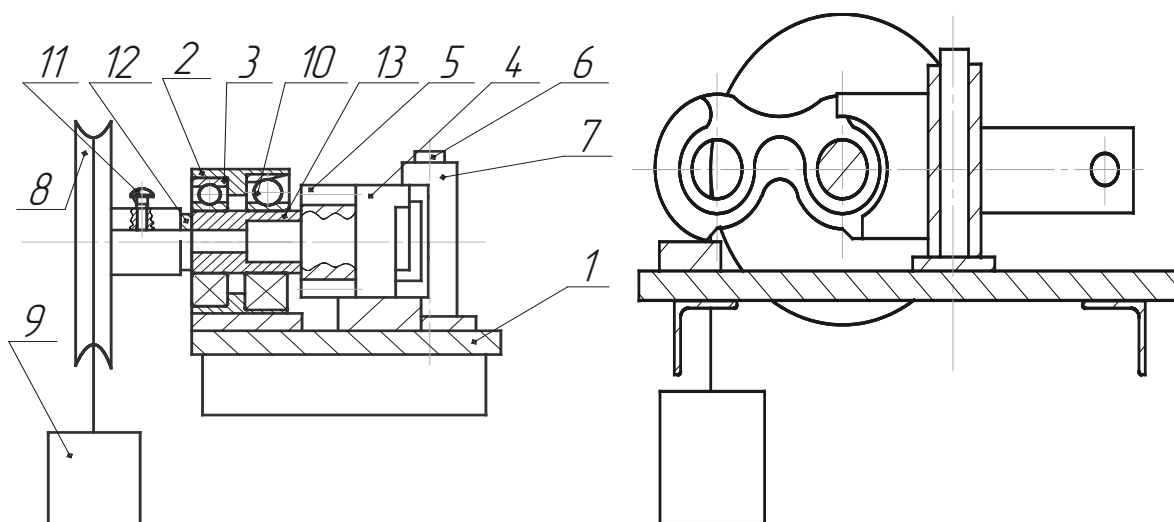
Установка для експериментального визначення коефіцієнтів тертя спокою: 1 — базова плита; 3, 10 — підшипники в корпусі 2; 4 — дослідний зразок підшипника ковзання; 5 — вал-шестірня; 6 — вісь; 7 — притиска вилка; 8 — шків; 9 — навантаження; 11 — фіксувальний гвинт; 12 — кільця; 13 — втулка
